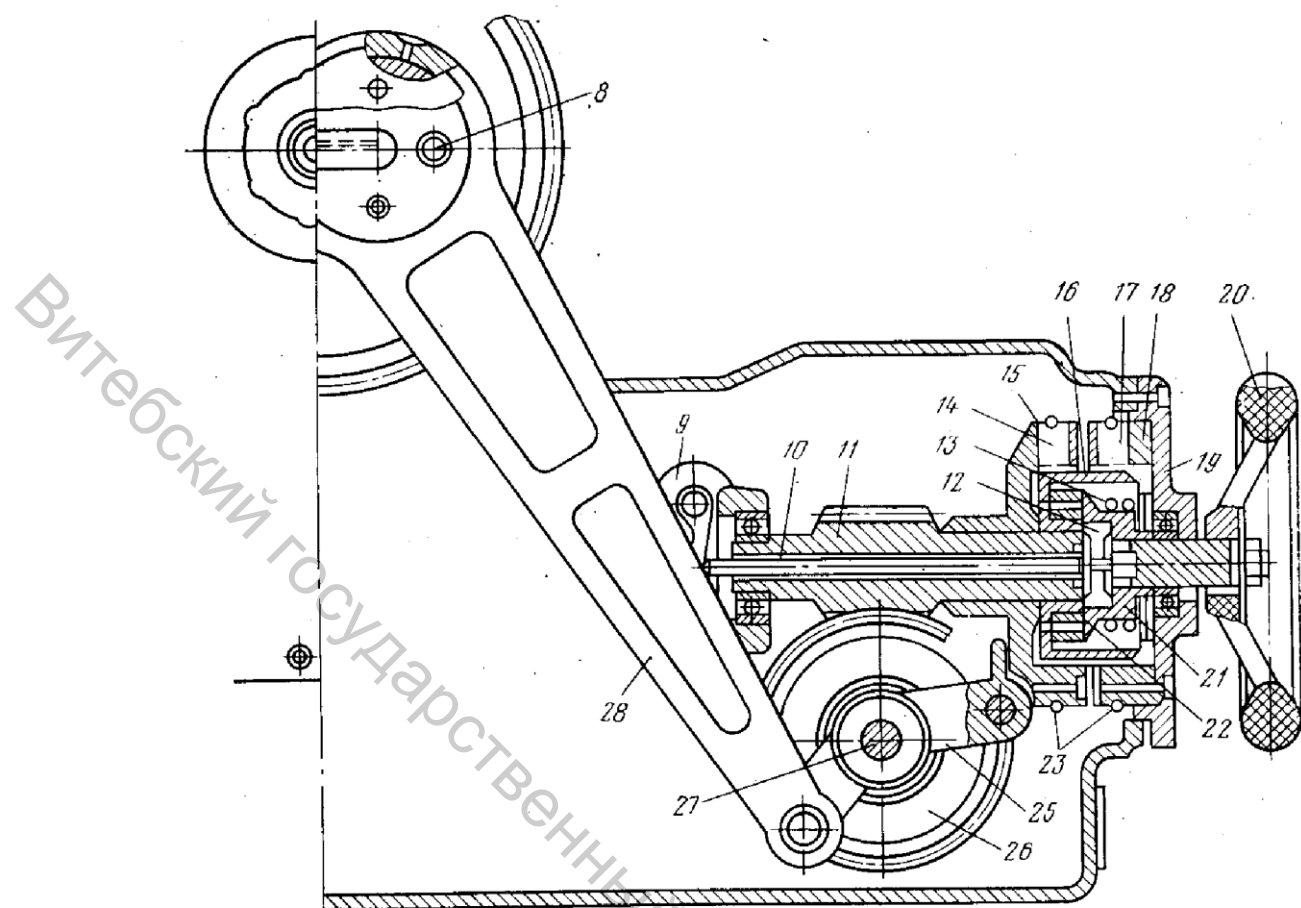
Товарный регулятор ткацкого станка П-105
